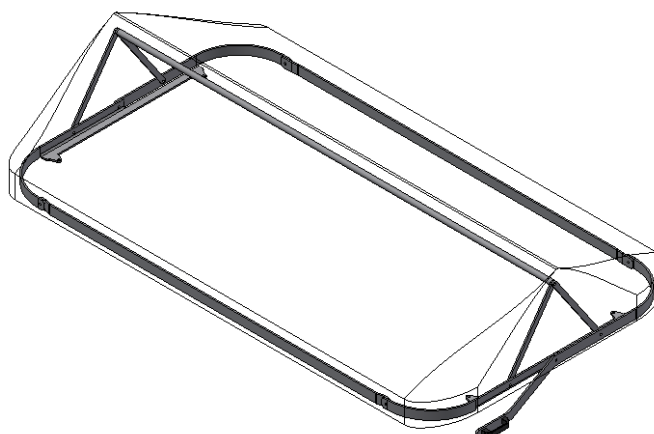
Tela de Cobertura c/ estrutura rebatível
